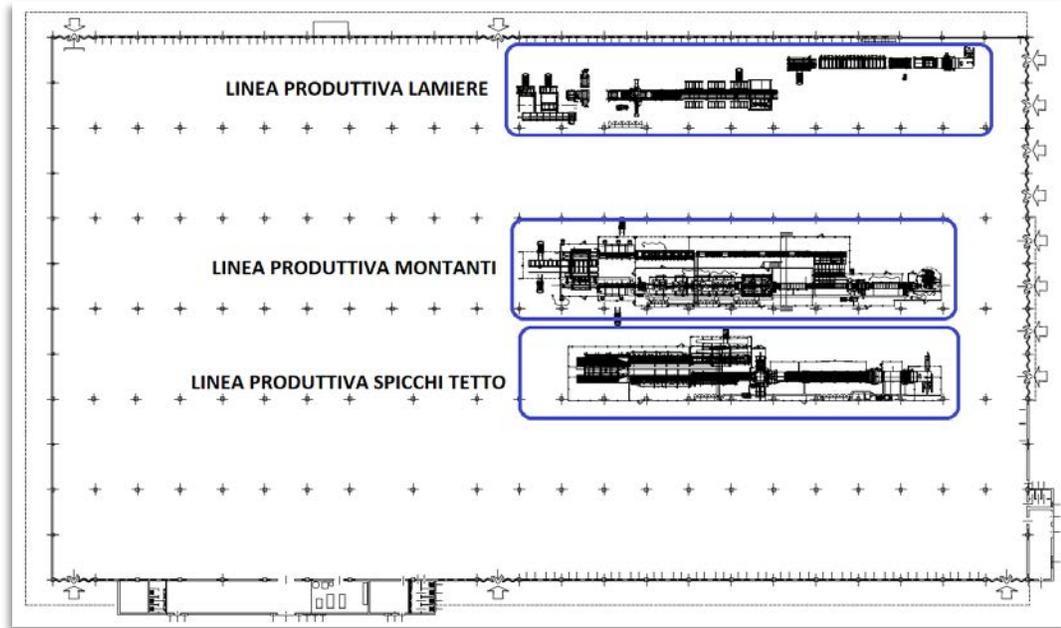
Layout definitivo stabilimento produttivo.
